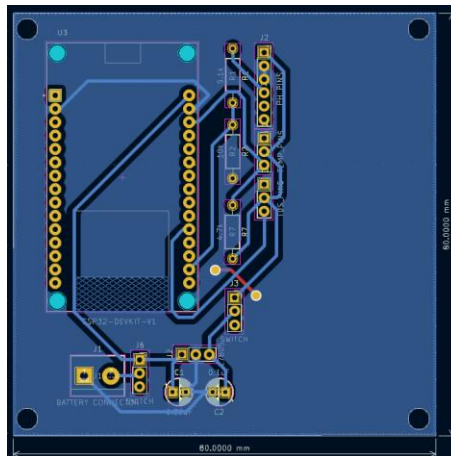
33 Diseño para la PCB del sistema de monitoreo de la calidad del agua.
